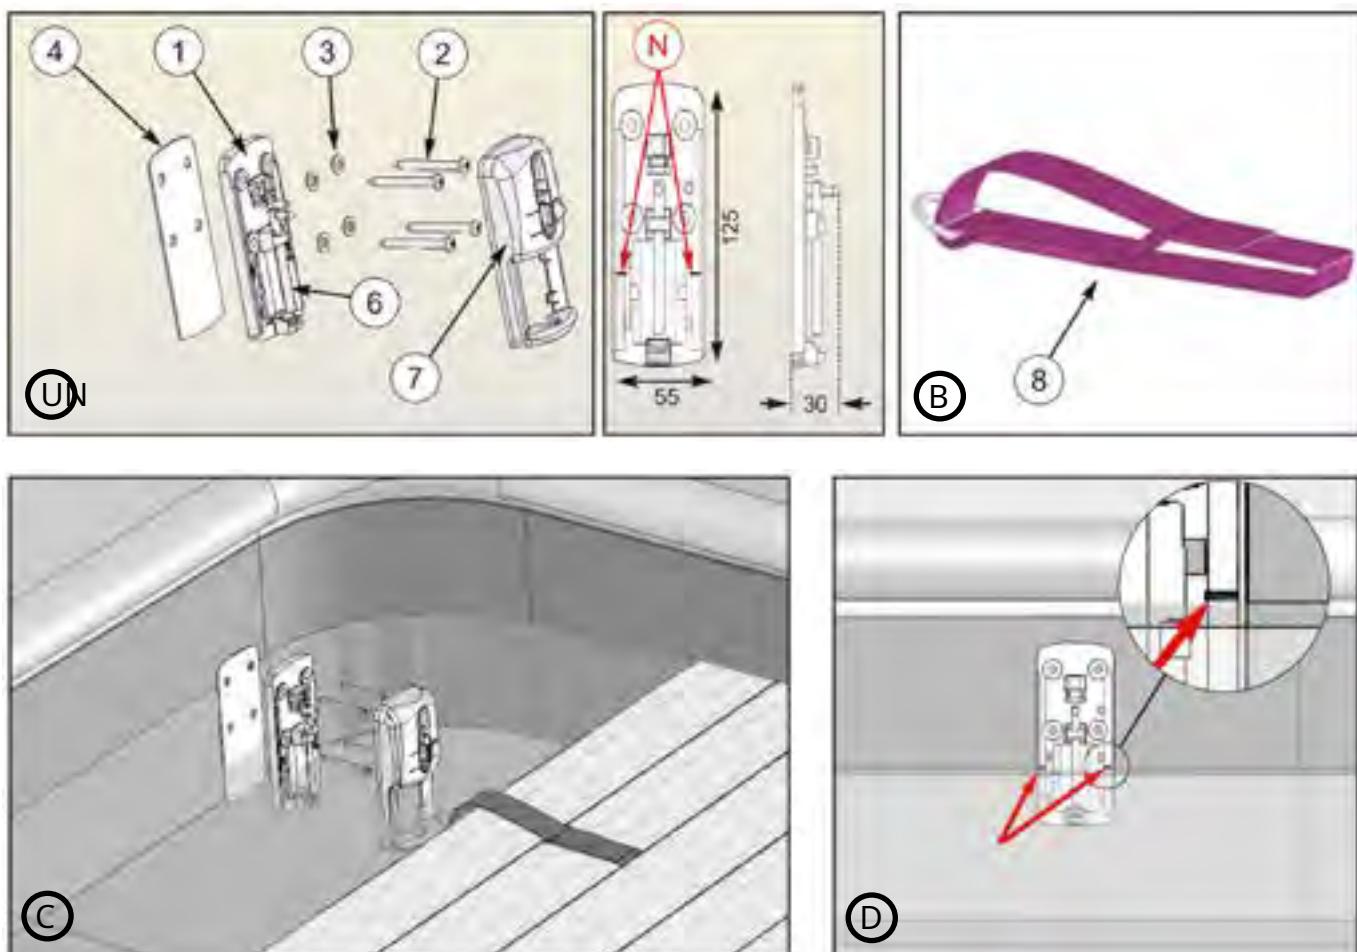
Montaggio degli elementi di fissaggio del coperchio
